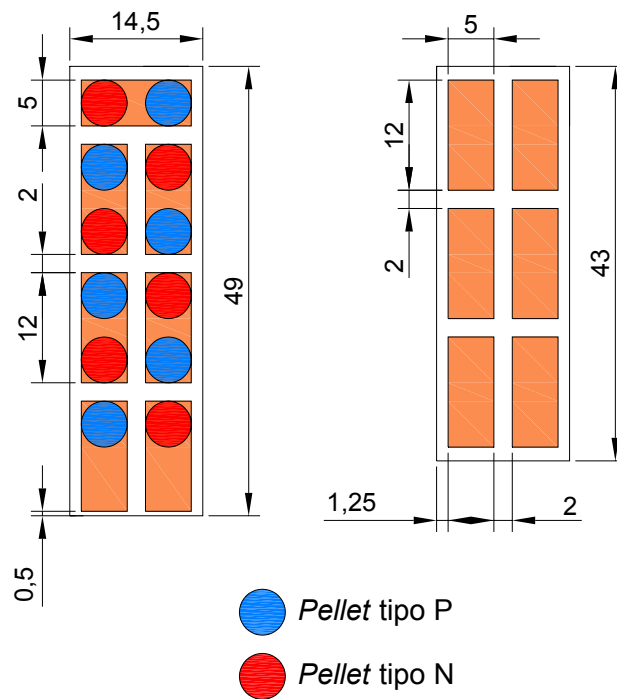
Dimensionado en mm de la parte inferior (izquierda) y de la parte superior (derecha).
